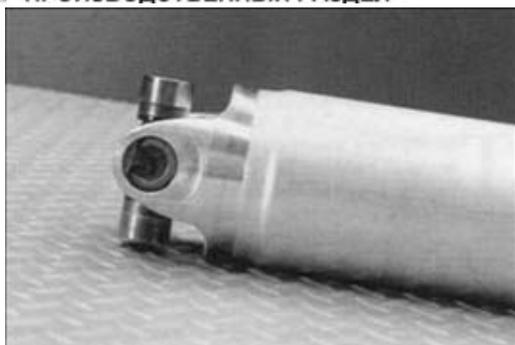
Алюминиевый (Al–Al) вал, сваренный способом МИС
